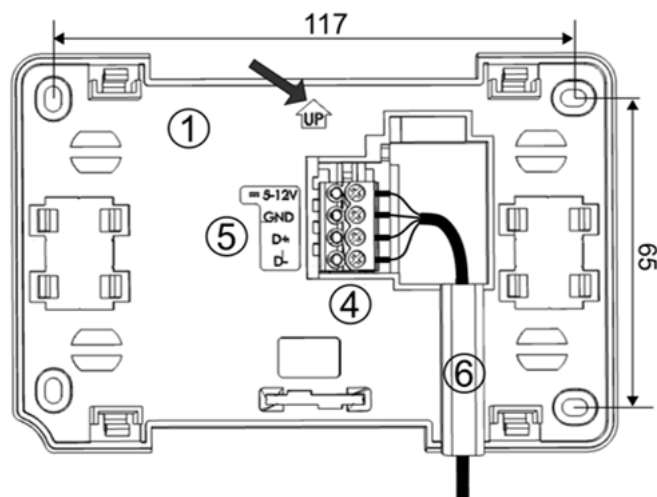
Bohrbild des Montagerahmens und Kabelanschluss
